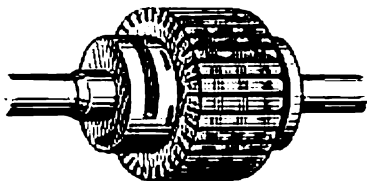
Induit non bobiné d'une machine à courant continu
